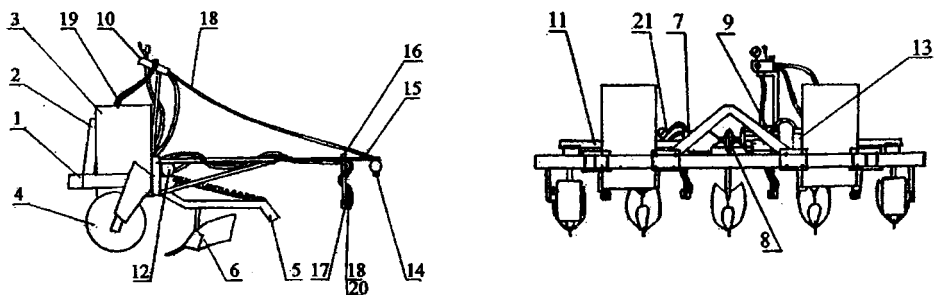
Схема культиватора-опрыскивателя: 1-рама; 2-сцепка; 3-емкость; 4-колесо опорное; 5-секция; 6-окучник; 7-гидромотор; 8-муфта; 9-насос поршневой; 10-регулятор-делитель, 11,12-гидро- и пневмораспределительные штанги; 13-фильтр; 14-гидравлическая штанга с распылителями; 15-удлинитель; 16-подвеска; 17-пневматический распылитель; 18,19,20-гидро- и пневмопроводы; 21-манометр; 22-компрессор; 23-ресивер.
